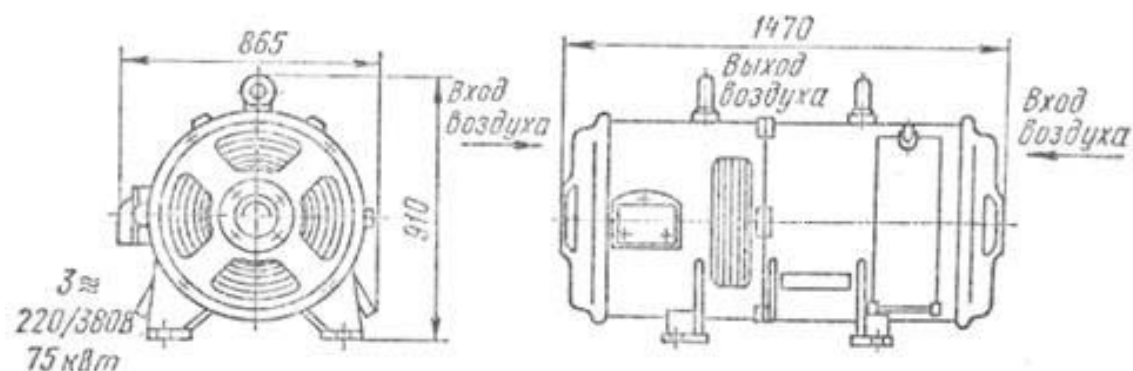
Преобразователь сварочный ПСМ-1000
